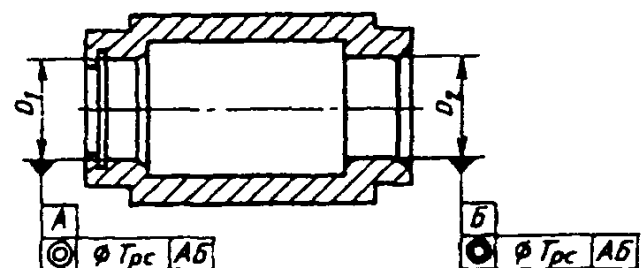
Обозначение допуска соосности посадочных мест корпуса относительно общей оси
